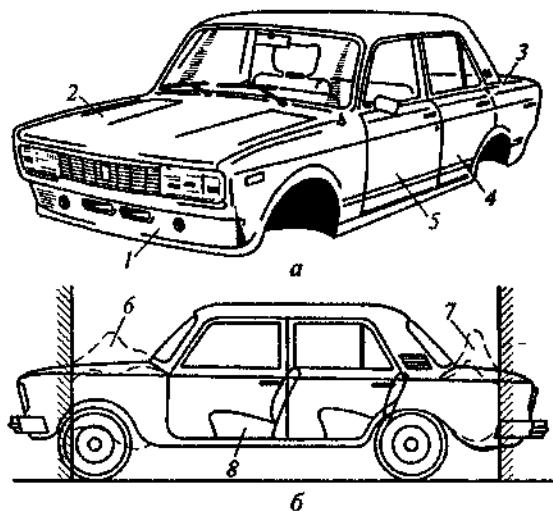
Кузов легкового автомобиля ВАЗ ограниченной проходимости: *а* — общий вид; *б* — деформации кузова при столкновениях; 1 — корпус; 2 — капот; 3 — крышка багажника; 4 и 5 — двери; 6 и 7 — части кузова; 8 — салон
